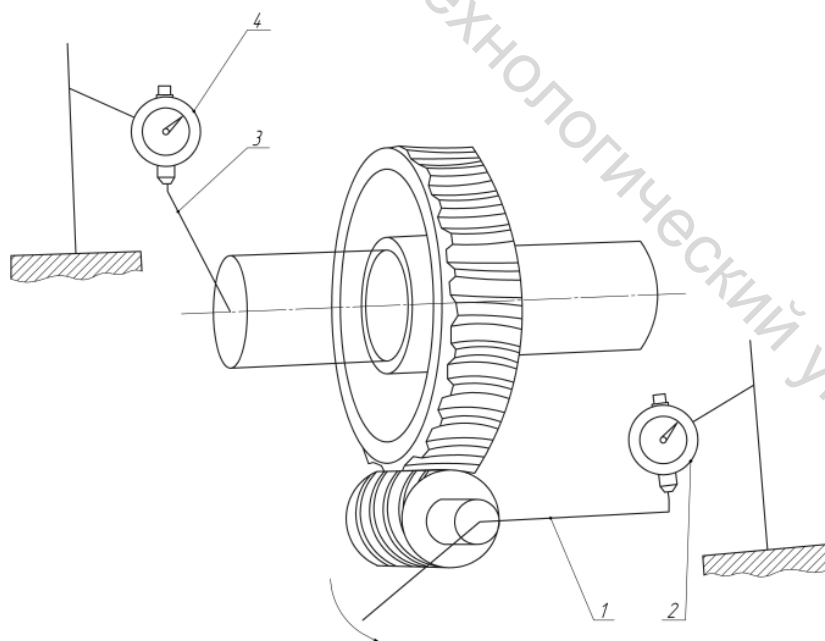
Схема измерения бокового зазора в червячном зацеплении
